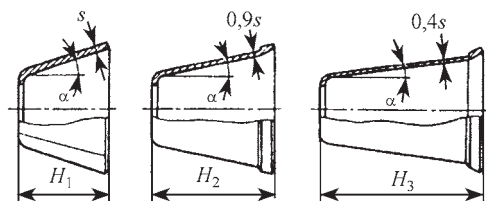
Технологическая схема изготовления длинномерной конической оболочки
